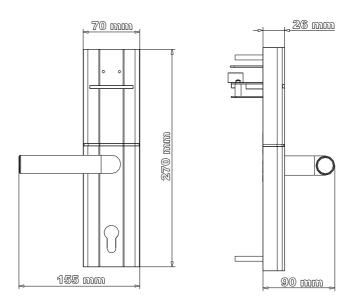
Dimensiones del alzado y perfil de la parte delantera de la cerradura.
